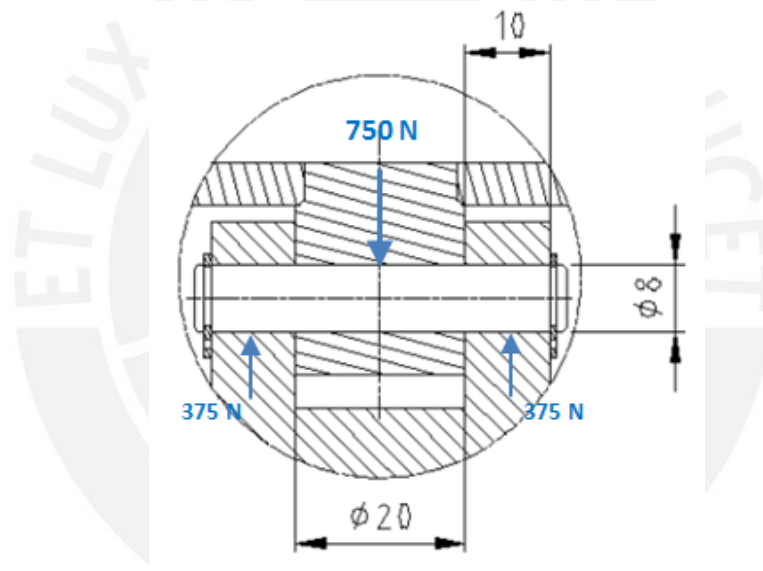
Cargas y dimensiones del pasador de la unión universal superior
